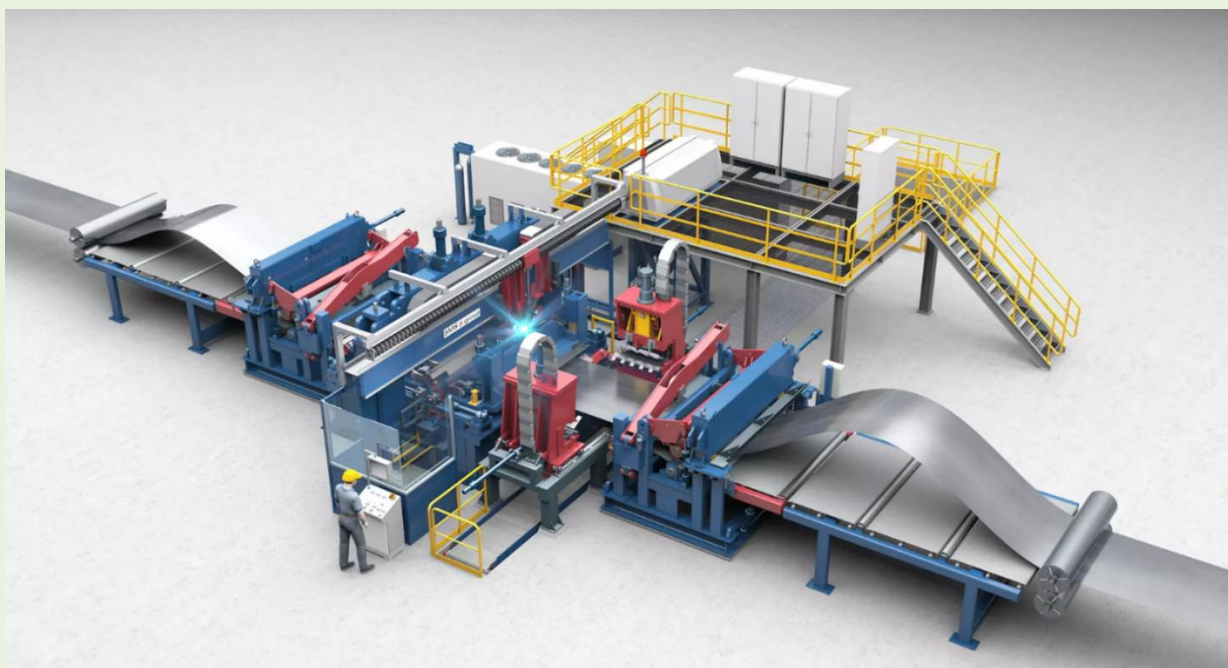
Imagem esquemática da máquina de solda a laser
